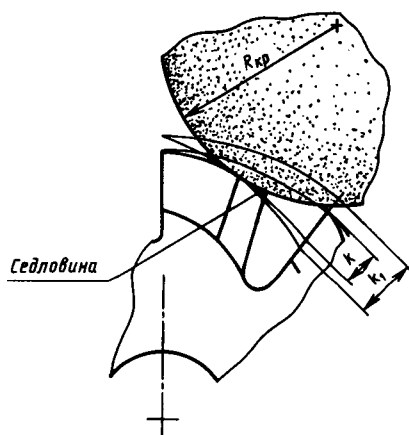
Двойное затылование фрез со шлифованным профилем
